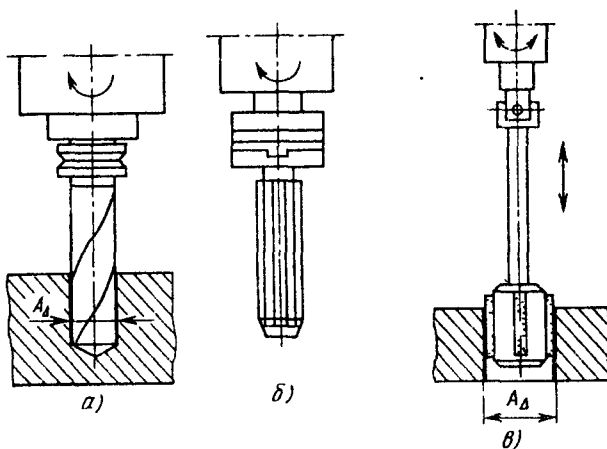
Схема получения размеров деталей мерными инструментами: а — сверлом, б — разверткой, в — хонинговальной головкой
